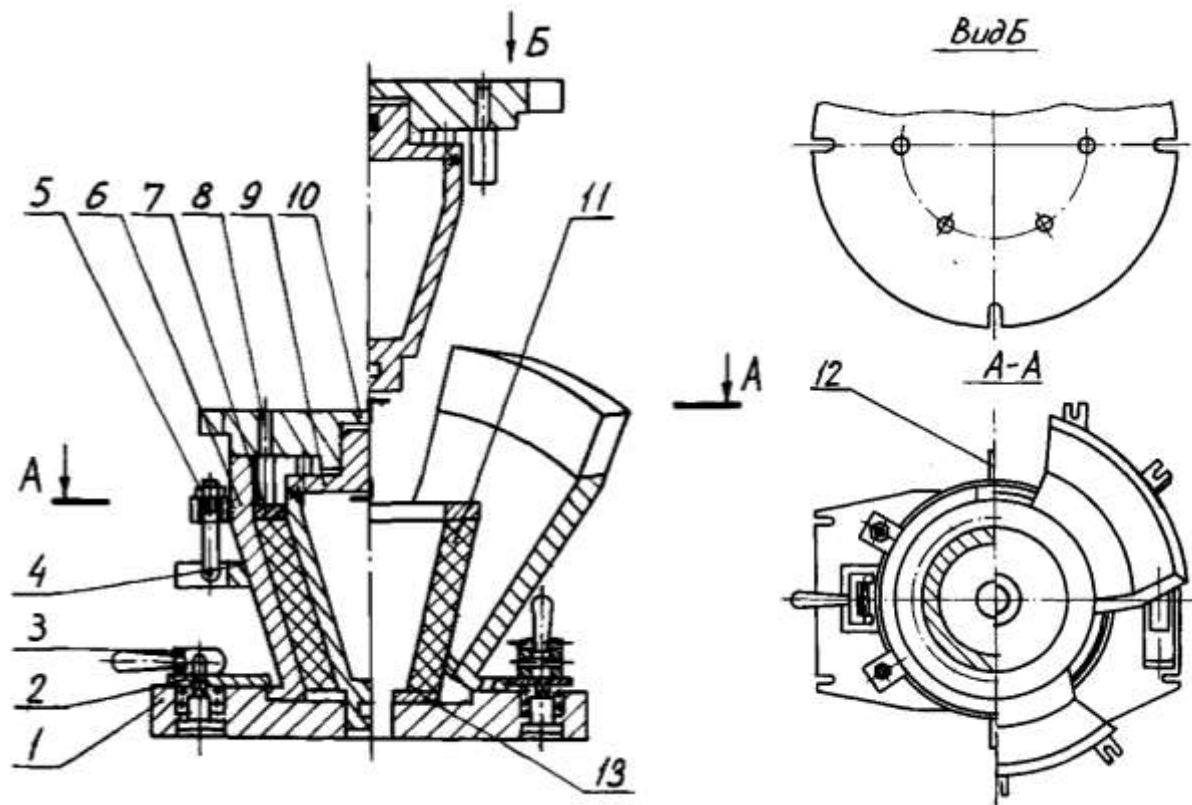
Конструктивна схема прес-форми з роз'ємною матрицею для пресування заготовок виробів типу „Конус”
